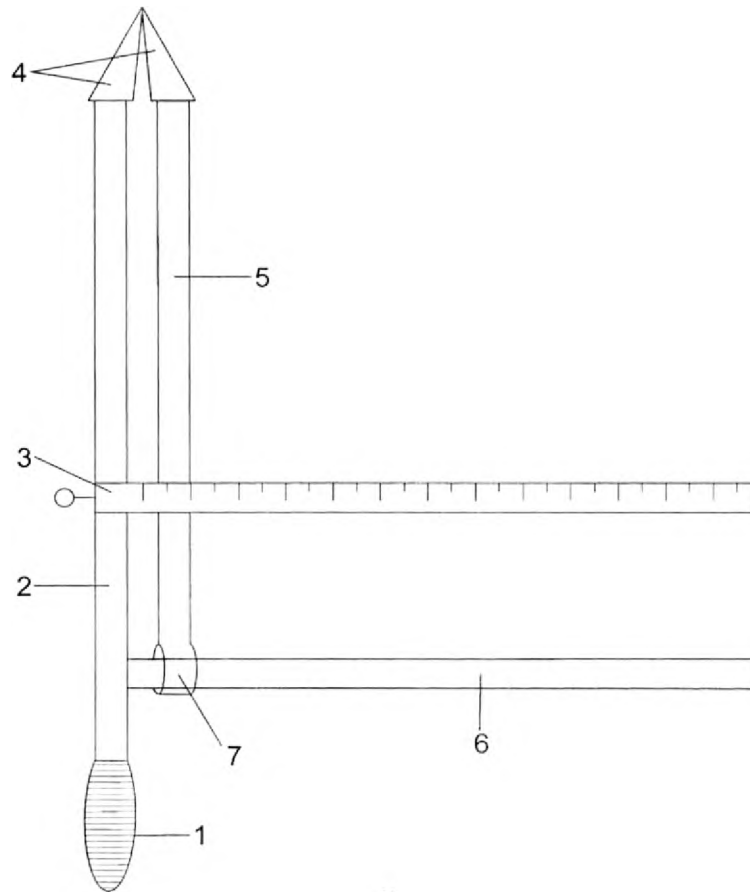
Схематичне креслення нової конструкції вимірювального циркулю.
